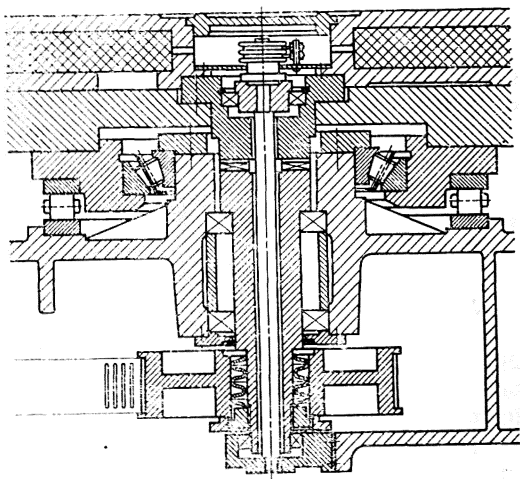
Шпиндельные опоры двухстоечного карусельно-шлифовального станка фирмы DÖRRIES
